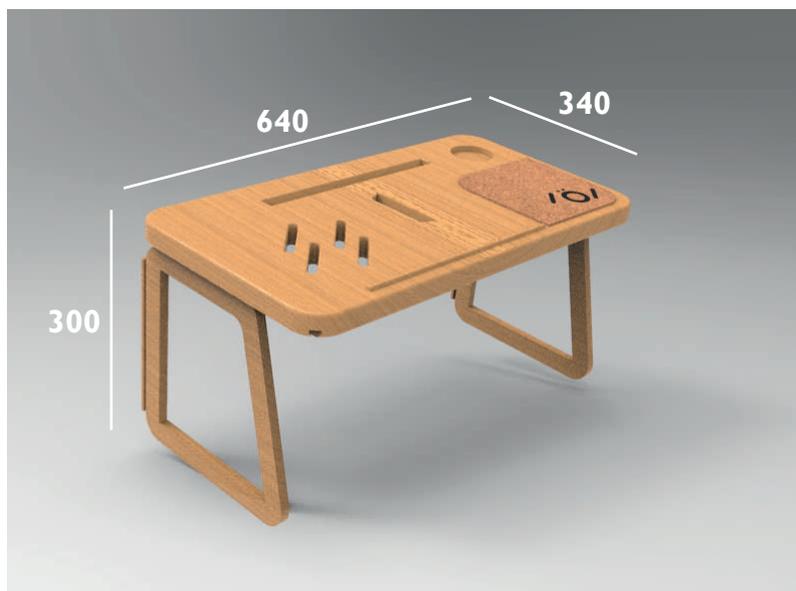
Dimensionado 1. Fuente: elaboración propia.
